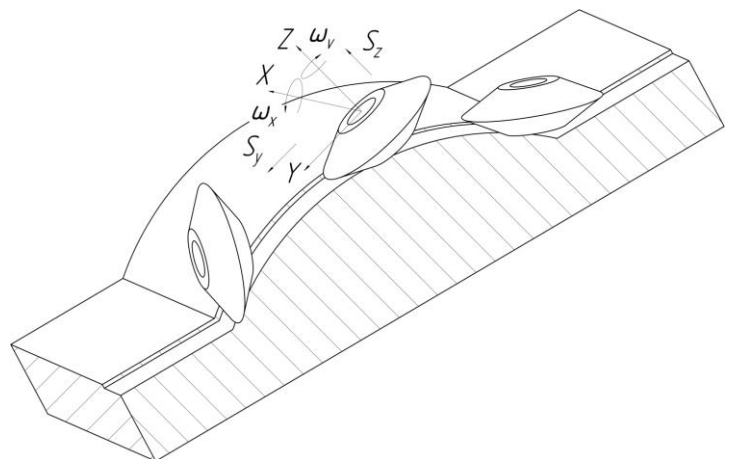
Схема обработки угловой двухсторонней фрезой
